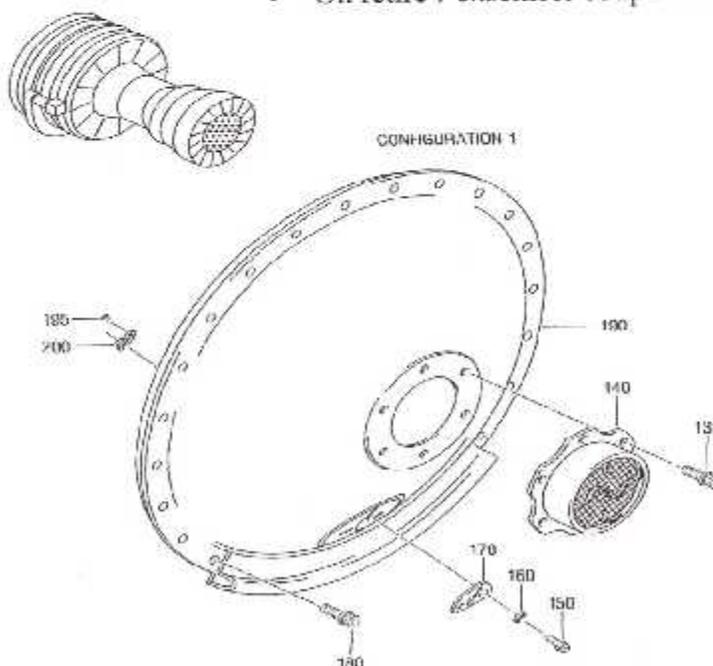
Dépose du Coupe- Feu et les Brides d'Assemblage.
